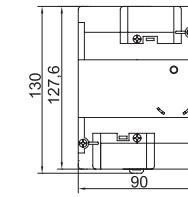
Габаритные и присоединительные размеры счётов габарита корпуса 1.
